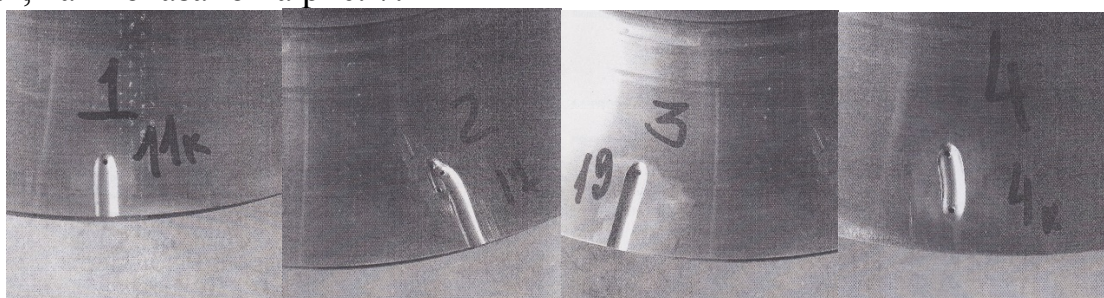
Разделка трещин под аргонодуговую сварку
